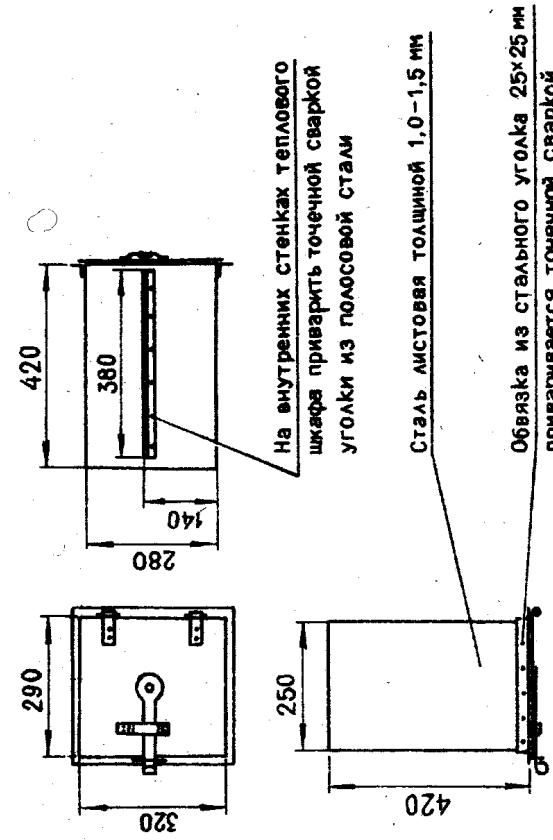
Тепловой шкаф для отопительно-варочной печи конструкции В. А. Потапова
